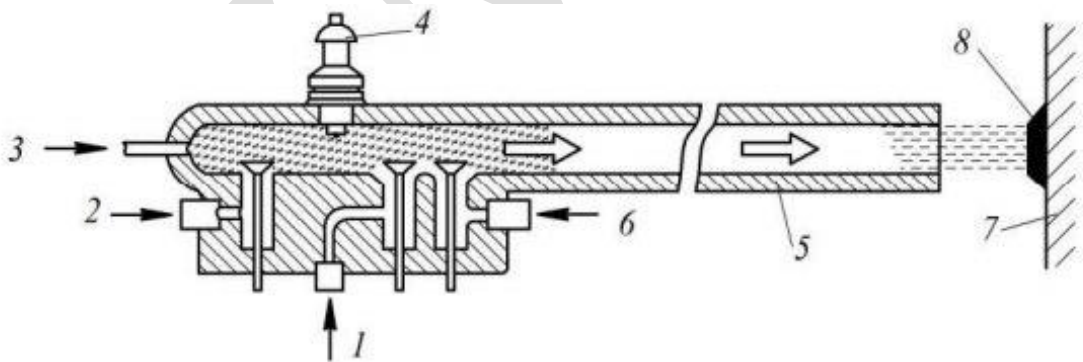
Схема детонаційного пристрою з внутрішнім суміші створенням: 1 – ацетилен; 2 – азот; 3 – подача порошку; 4 – свічка запалювання; 5 – вихідна труба; 6 – кисень; 7 – деталь; 8 – пляма покриття [17]
